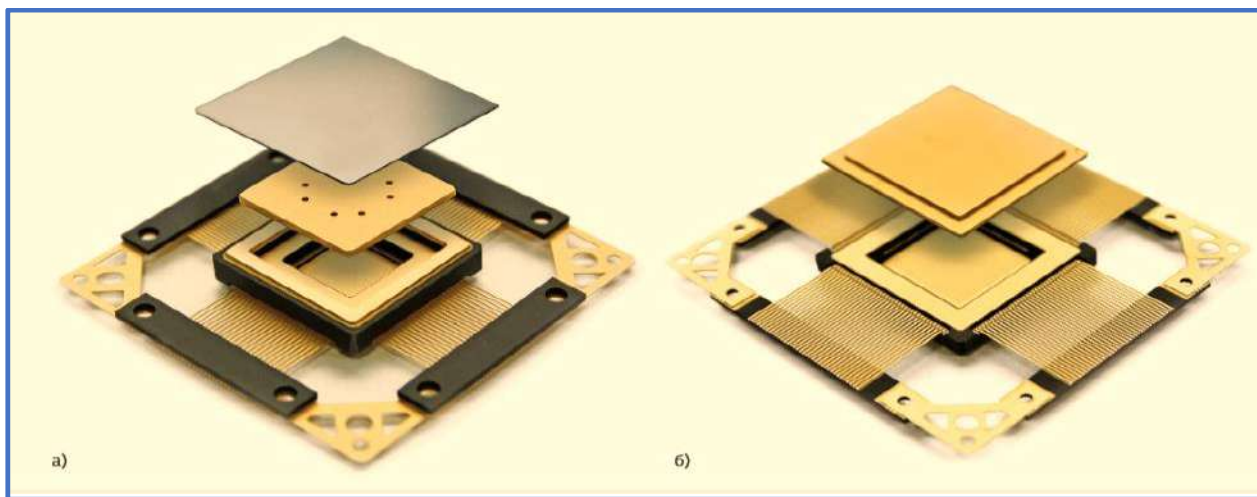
Варианты металлокерамического корпуса ИМС с интегрированным ЭРЗ на основе композитного материала W-Cu: а) 100-выводной планарный корпус с герметизацией пайкой, б) 144-выводной планарный корпус с герметизацией шовно-роликовой сваркой
